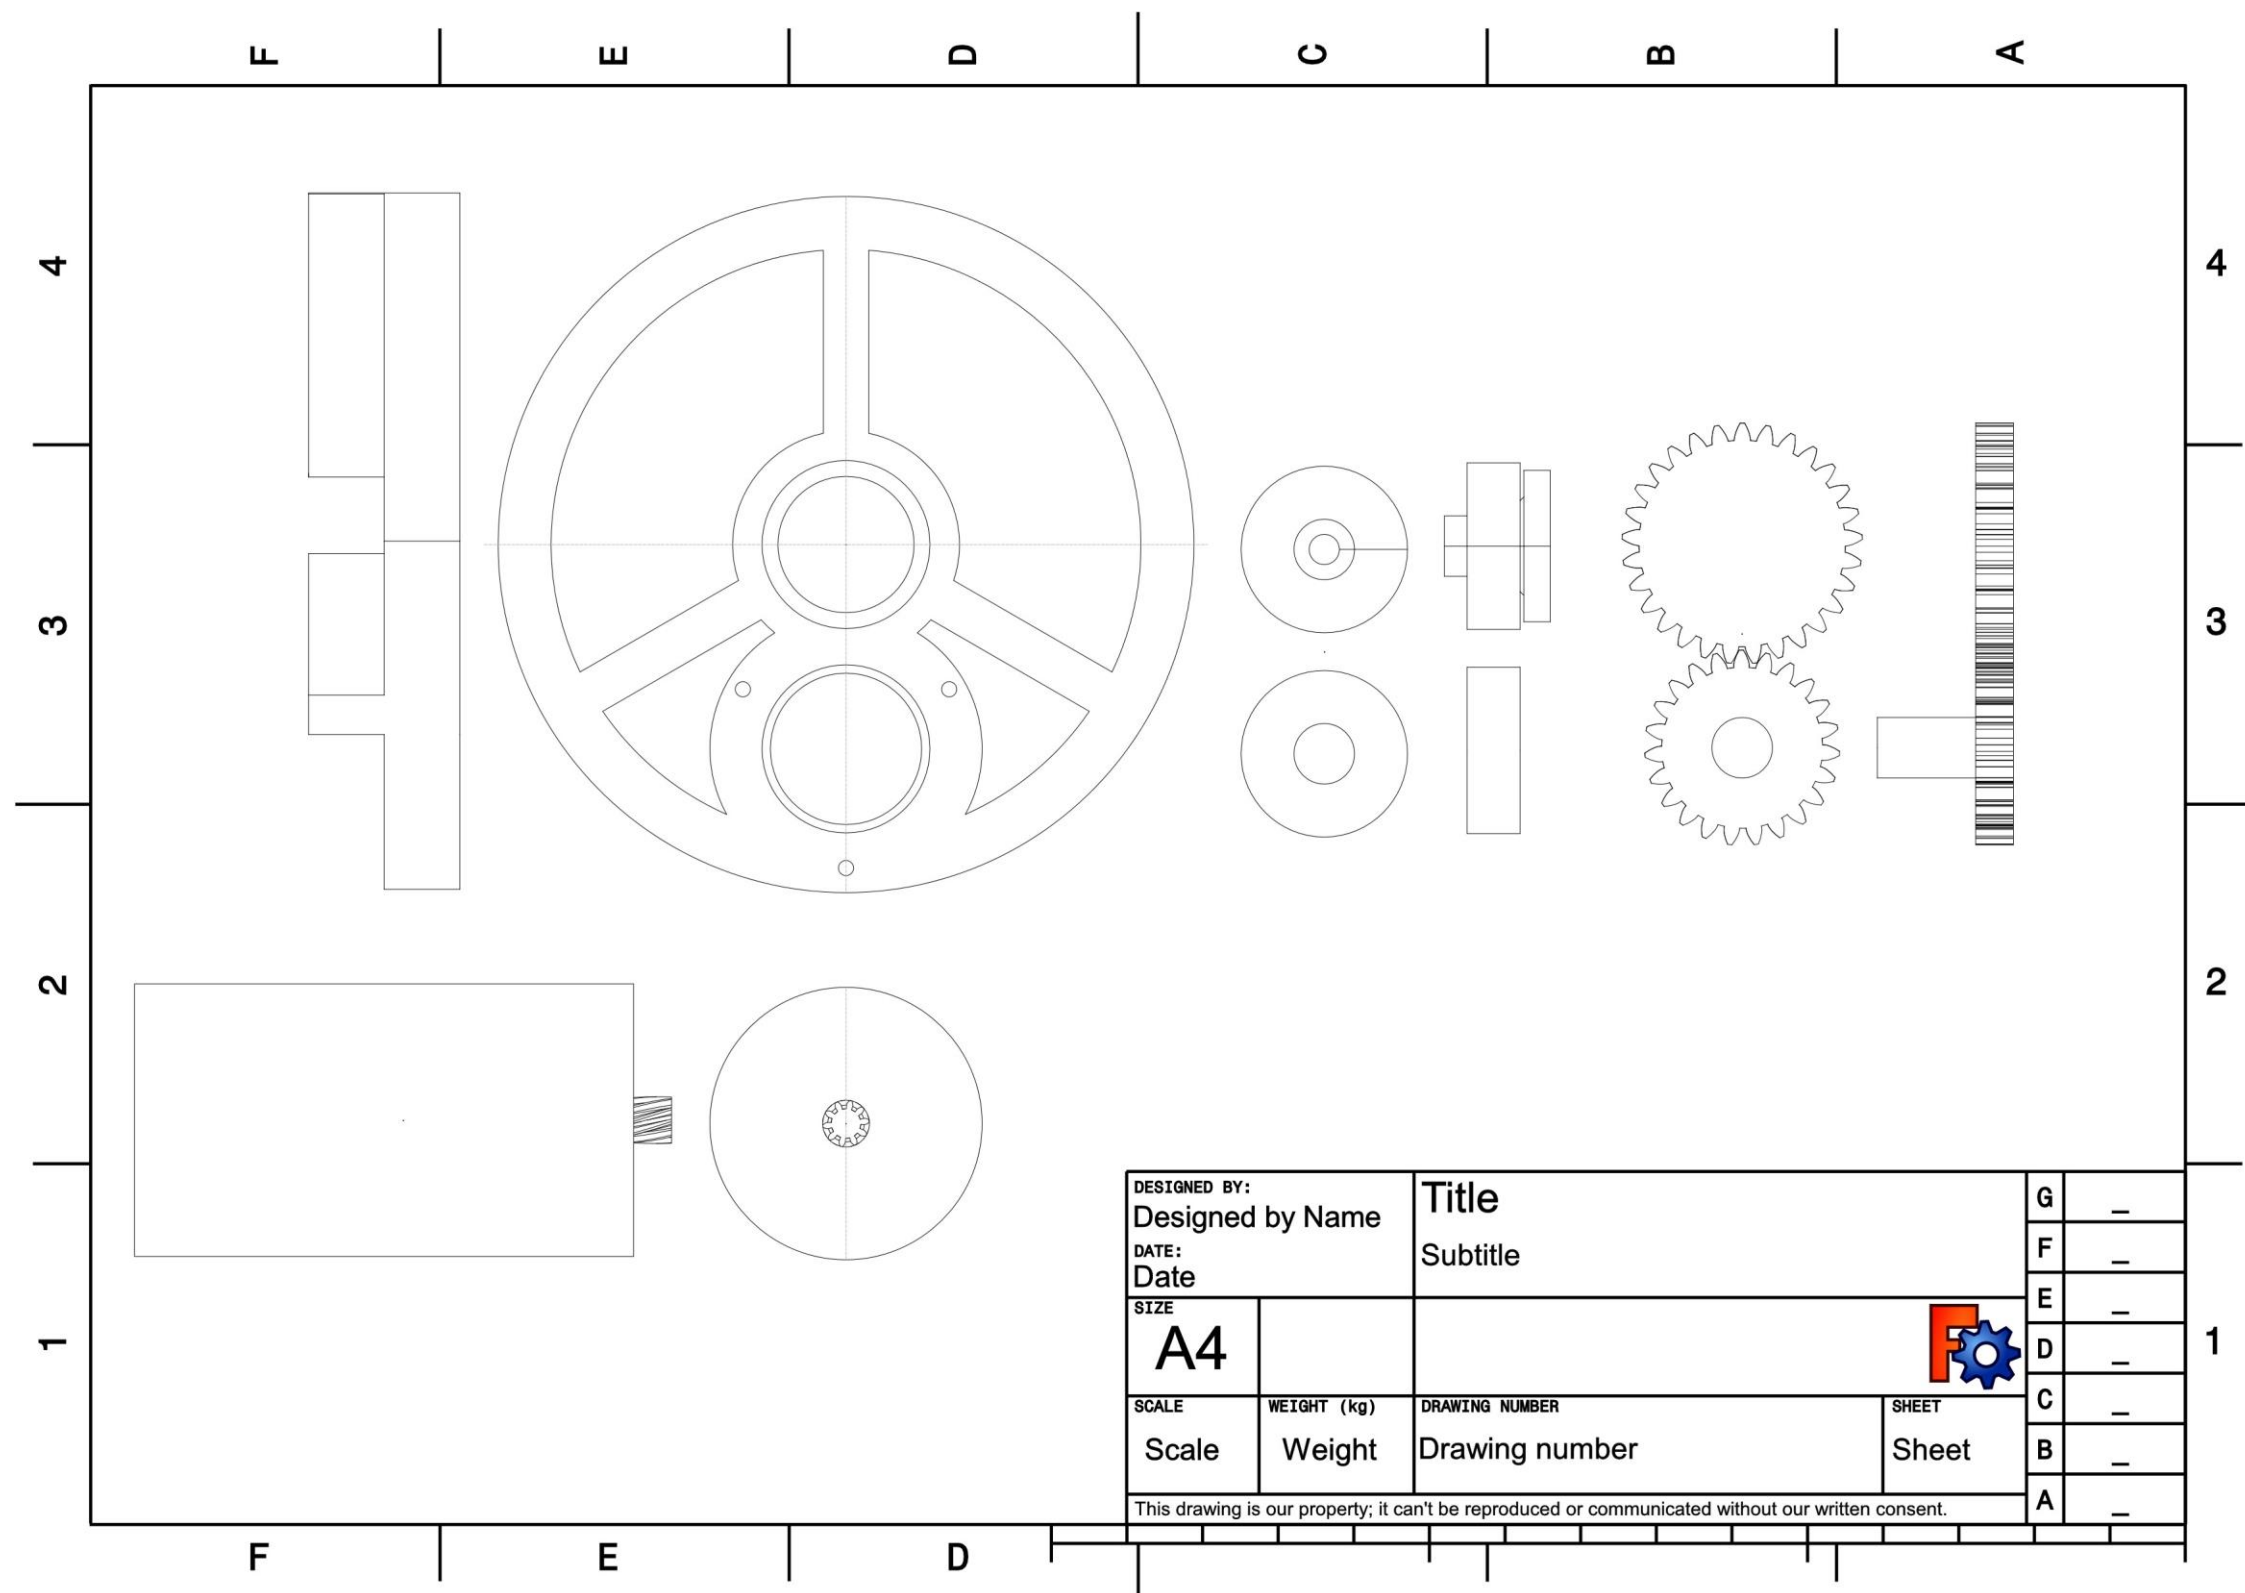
Soporte motor inundación 3 Engranajes Fuente Propia.
